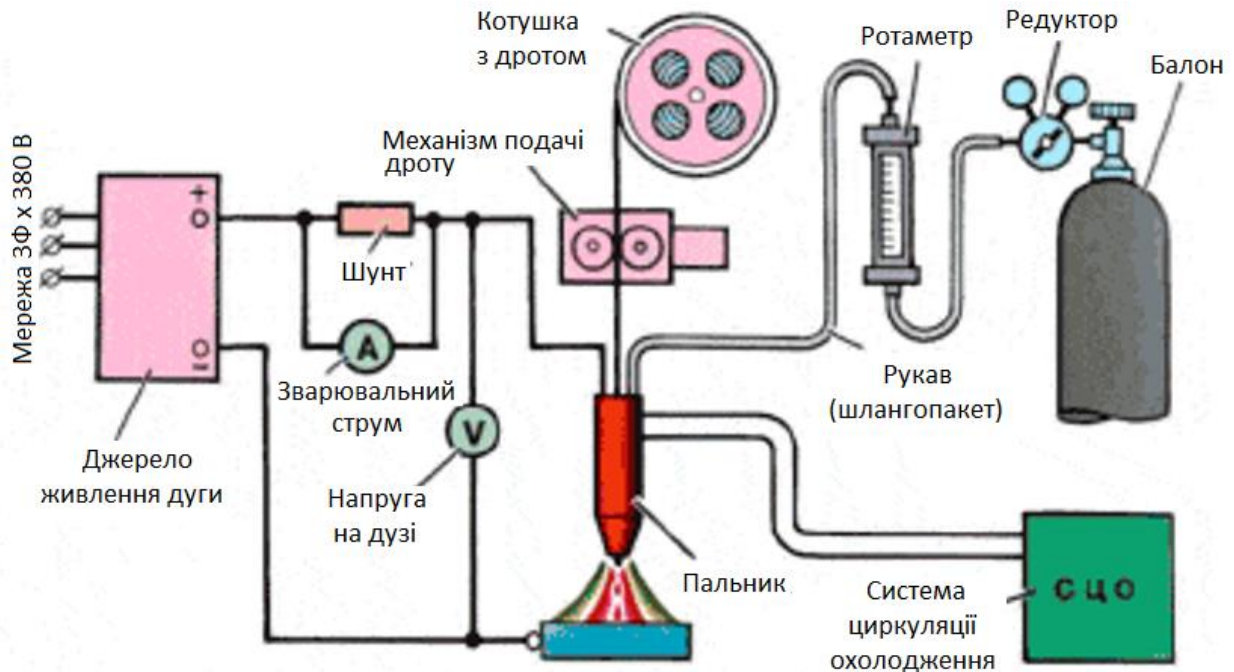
Схема установки для зварювання в середовищі захисних газів
